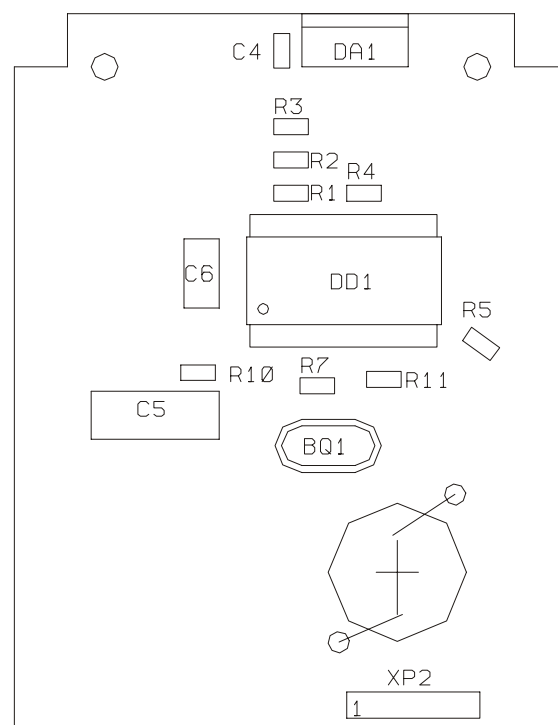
Сборочный чертеж платы обработки блока датчика ФСТ (СО). Сторона пайки.
